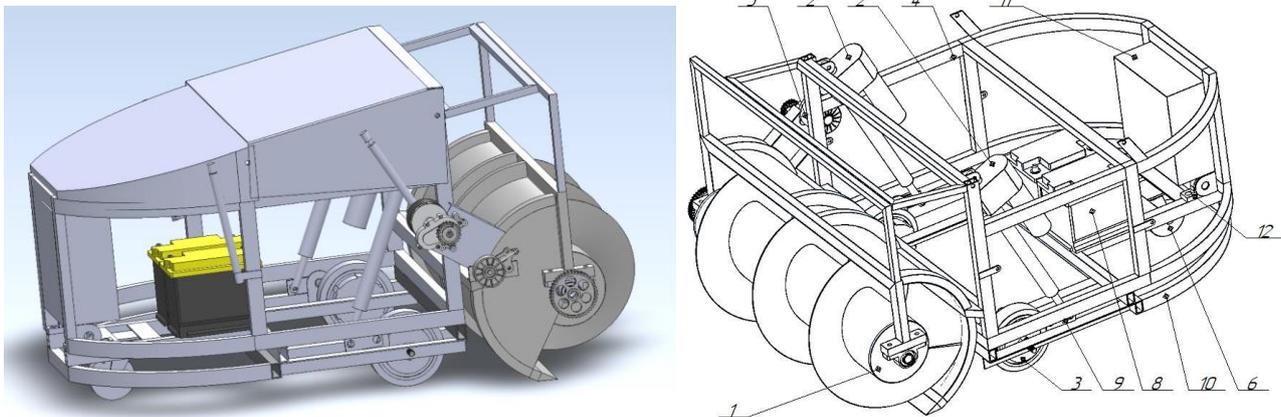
Общий вид подталкивателя кормов: 1 – шнекоротор; 2 – линейный электропривод; 3 – ведущее мотор-колесо с редуктором; 4 – рама верхняя; 5 – привод шнекоротора; 6 – колесо опорное поворотное; 7 – ремень приводной шнекоротора; 8 – аккумулятор; 9 – планка компенсационная; 10 – рама нижняя; 11 – ящик электрооборудования; 12 – подшипник корпусной
